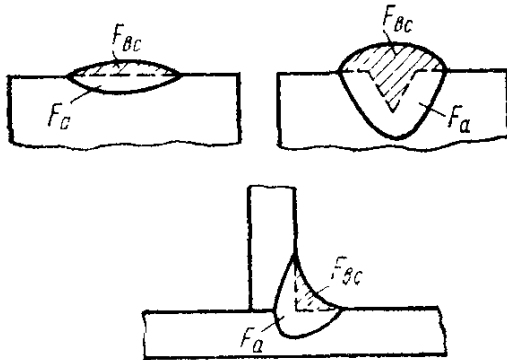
Площади проплавления F_a и наплавки F_{bc} для различных типов сварных соединений при дуговой сварке плавлением
